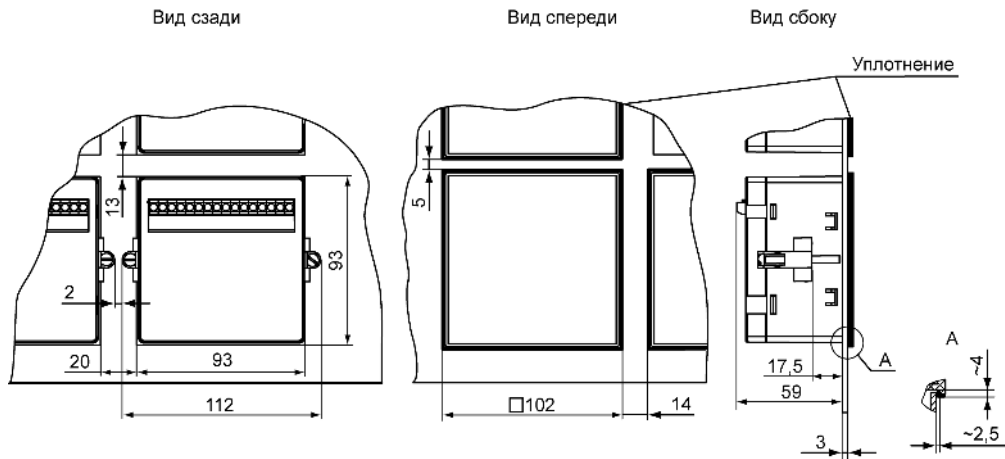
Прибор в корпусе Щ1, установленный в щит толщиной 3 мм
